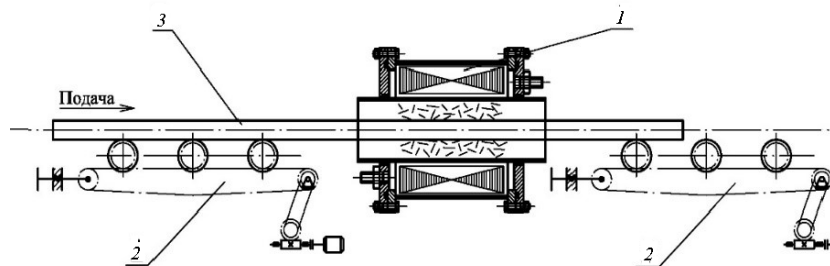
Технологическая схема магнитодинамической обработки длинномерных деталей: 1 – рабочий блок устройства с ВЭМП; 2 – механизм перемещения детали; 3 – деталь
